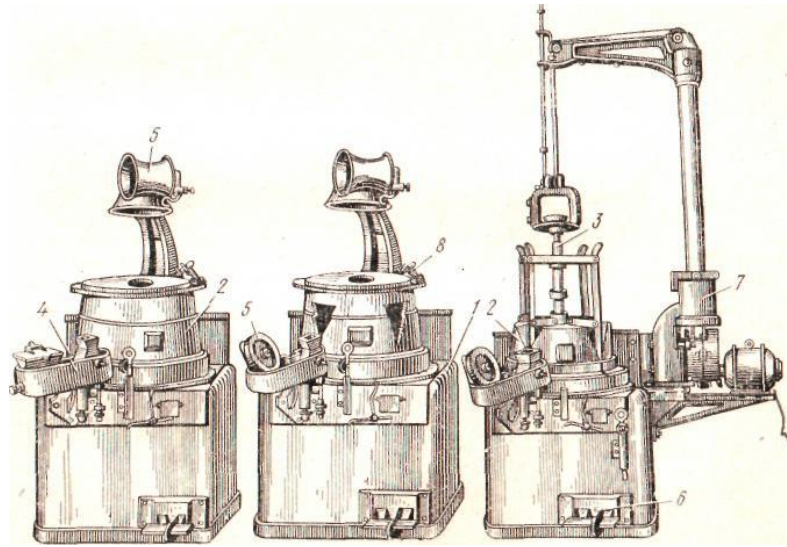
Блокова волочильна машина: 1 - станина блоку; 2 - барабан; 3 - знімач; 4 - мильниця з волокодержателем; 5 - направляючий ролик; 6 - педаль включення і виключення; 7 - знімний пристрій; 8 - поводок; (двигуни, коробки швидкостей і варіатори розташовуються за блоками машини)
